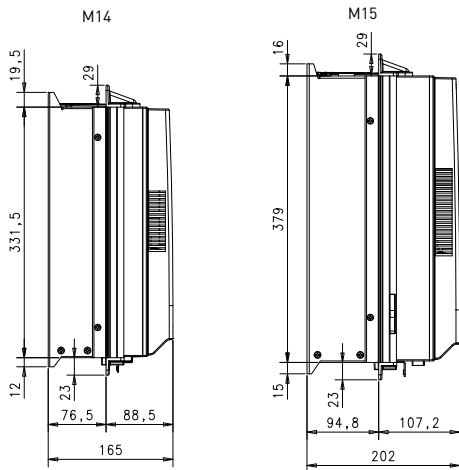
Размеры углубления для фланцевого крепления приводов типоразмеров M14 и M15 (ед. изм.: мм)
